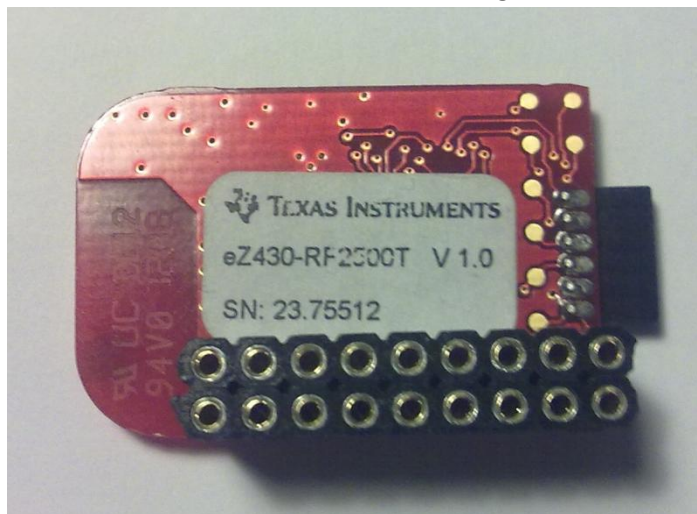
M dulo MSP430 RF2500 con el conector soldado
